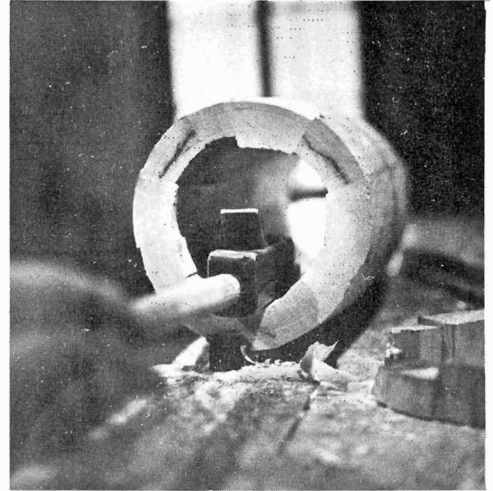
Links: KONRAD GIETEL bearbeitet ein Holzstück mit einem Beil zu einer Daube; oben: die Innenflächen des Fasses werden gehobelt
